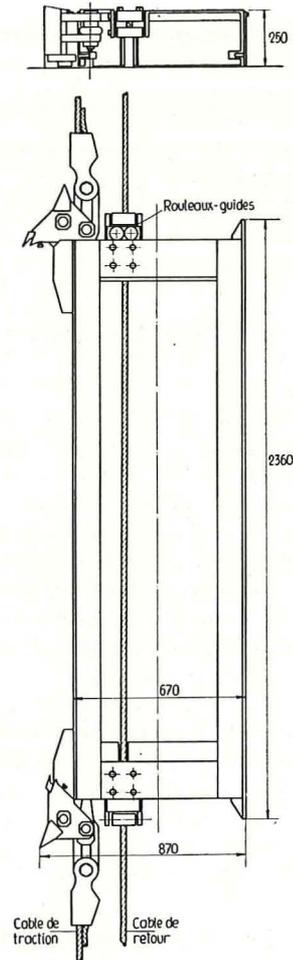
is. — Coupe et vue en plan du scraper-rabot.
